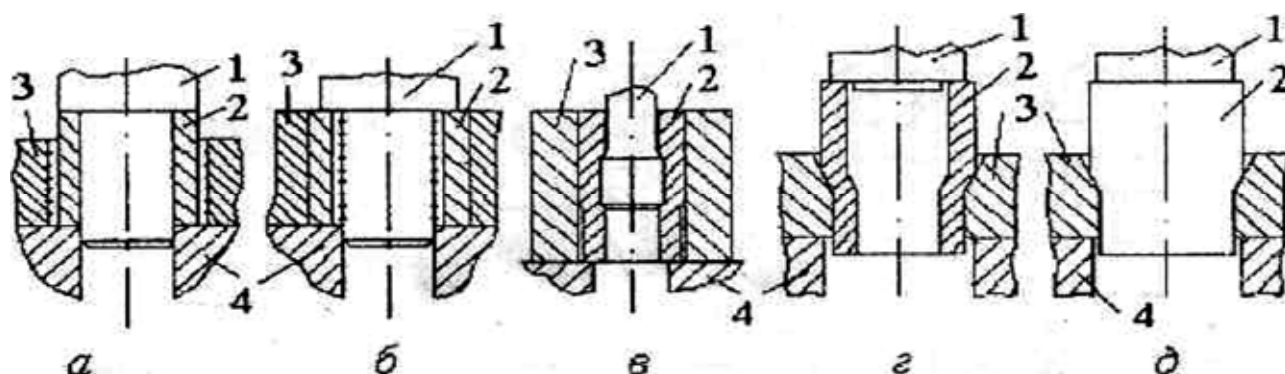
Схемы оборудования для восстановления размеров деталей пластичной деформацией: а и б - осадка с увеличением наружного с уменьшением внутреннего размеров; в - раздача; г - обжатие; д - вытяжка; 1 - пуансон; 2 - деталь; 3 - матрица; 4 - плита
